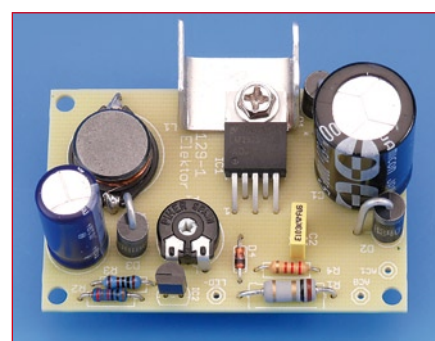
Voilà à quoi ressemble le prototype. Le refroidissement est assuré par un petit morceau de tôle d'aluminium sur lequel IC1 est vissé.
